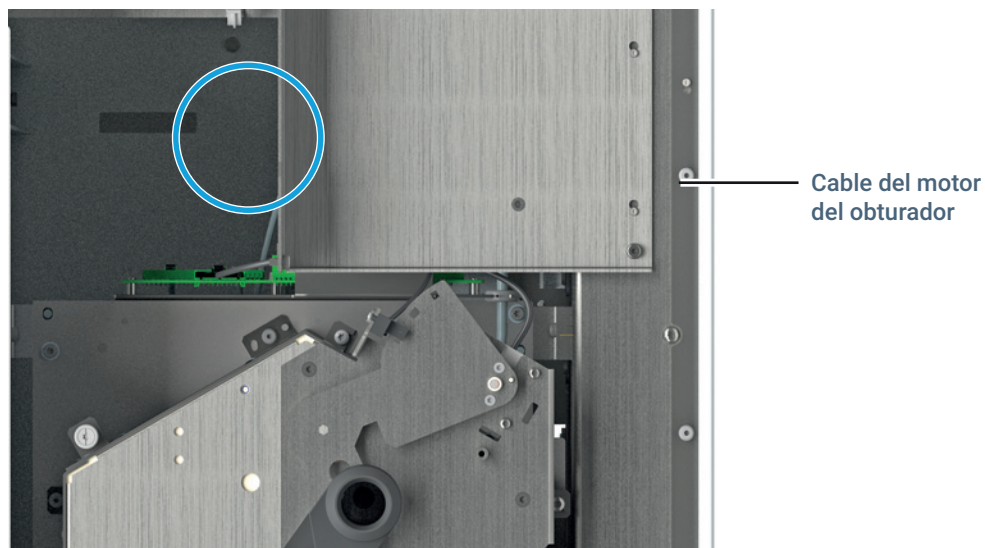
Desconecte del tablero de conector el cable del motor del obturador
